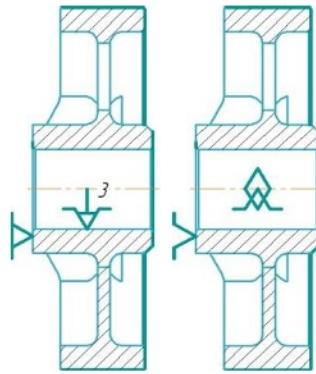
Умовна та теоретична схема базування зубчастого колеса
